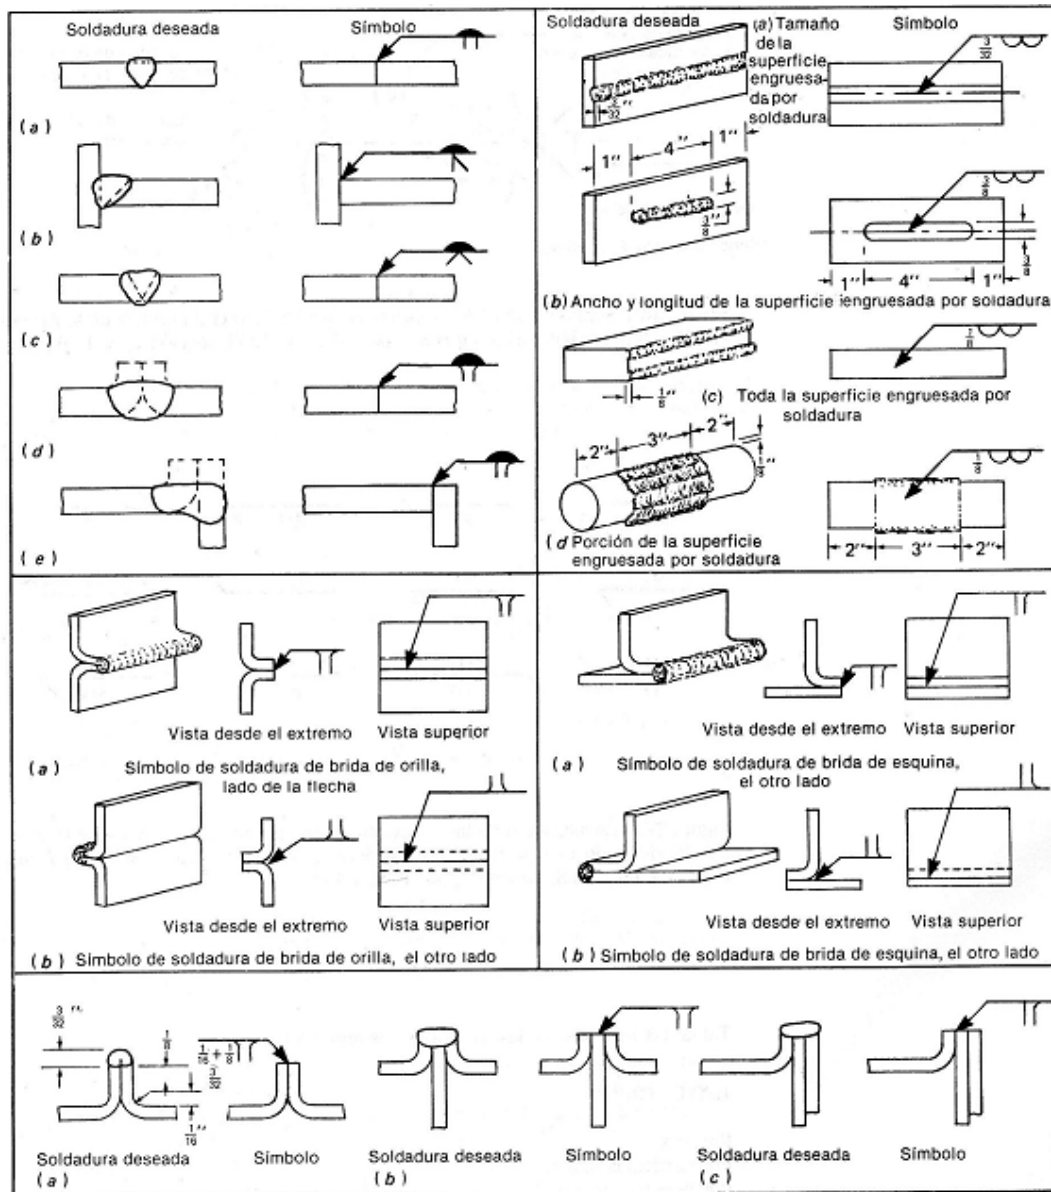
Ejemplos de símbolos de soldaduras y las soldaduras que representan.
